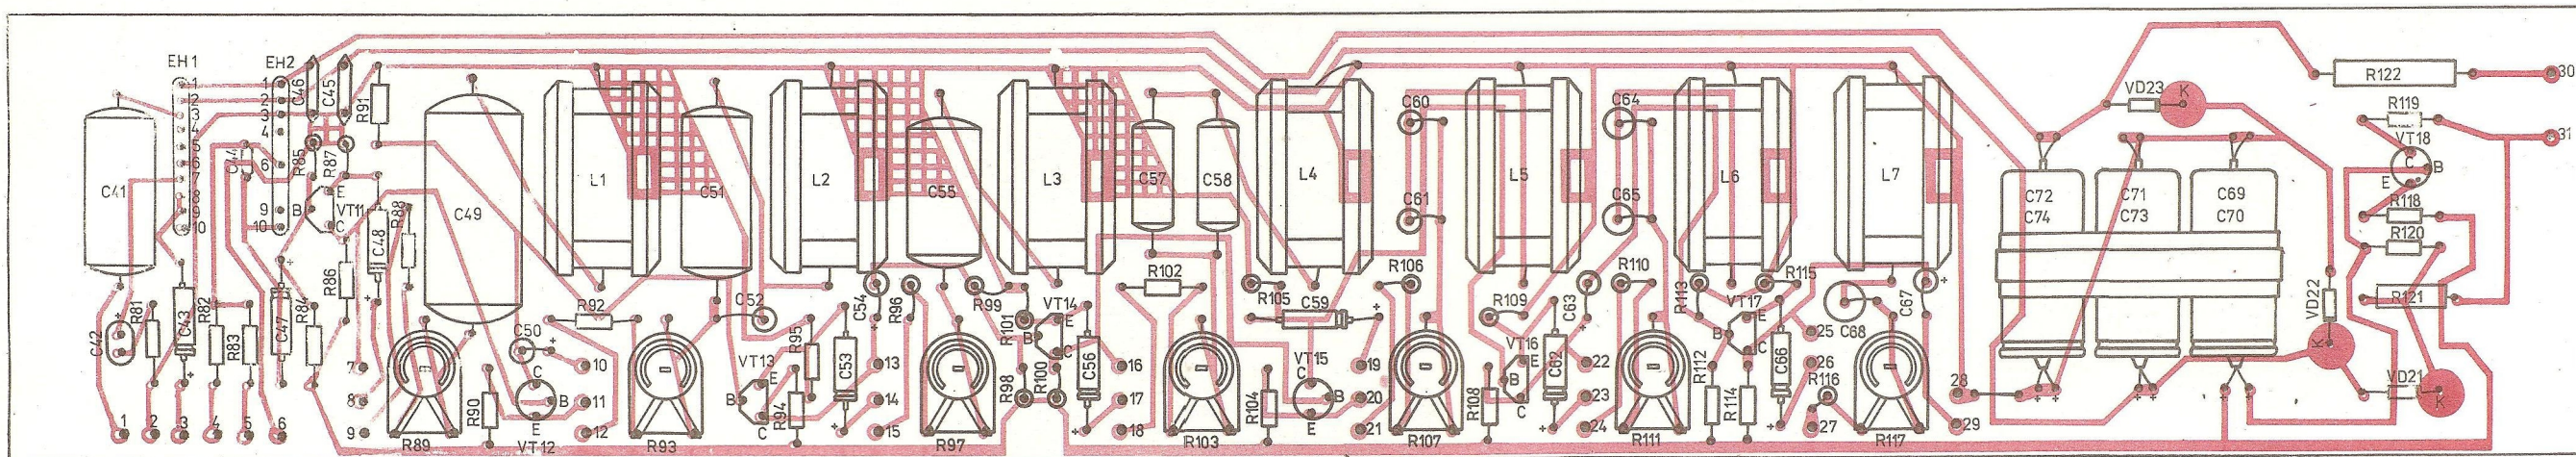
Deska modulometru 3AK 051 20 (strana spojů)
